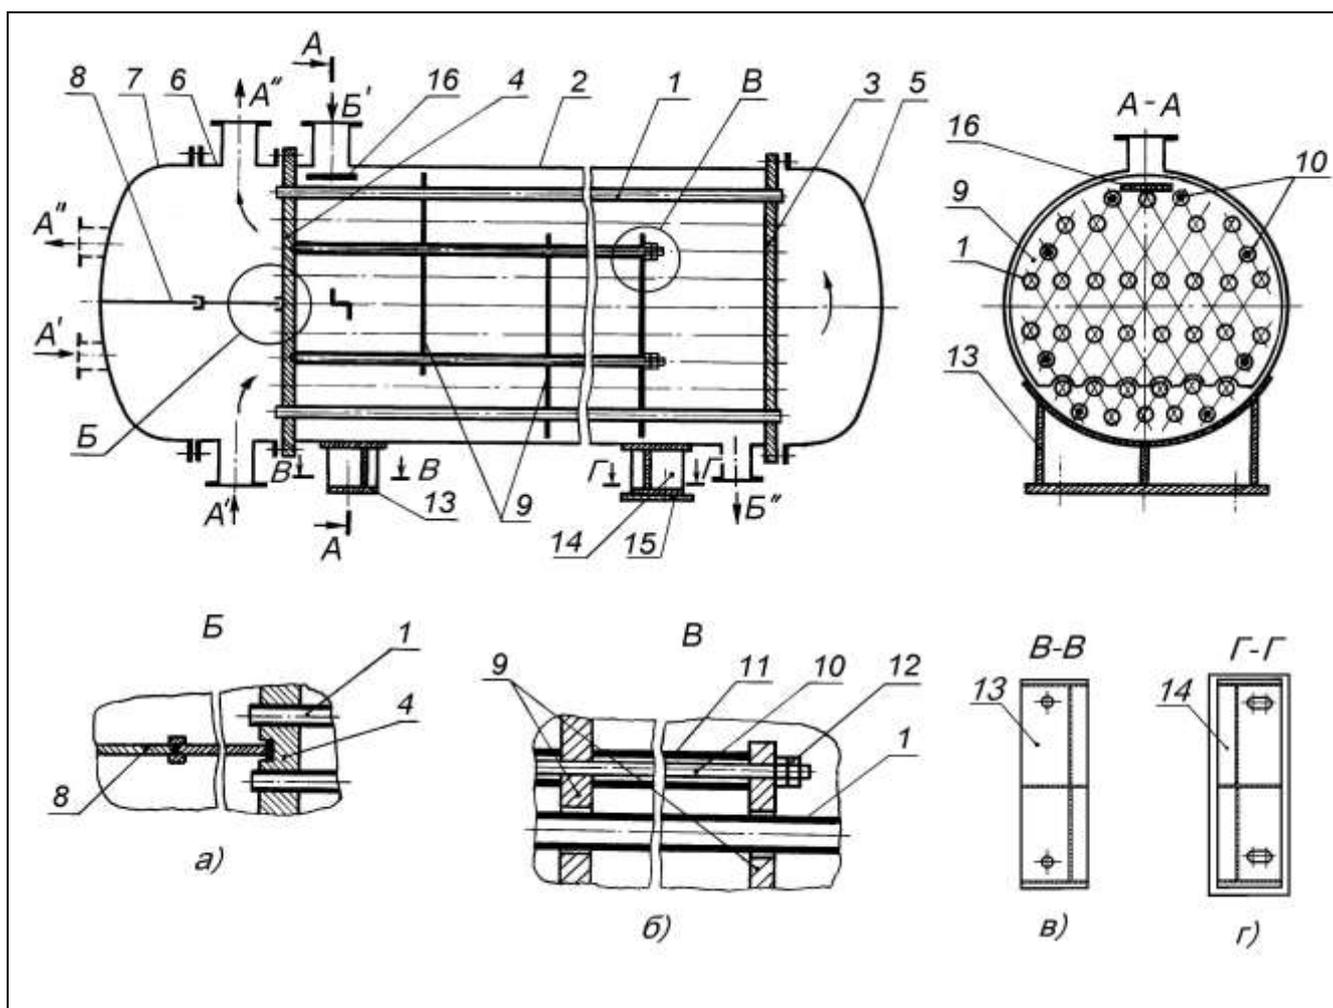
Теплообменник жесткой конструкции с неподвижными трубными решетками типа Н: а) – узел соединения продольной перегородки 8 с трубной решеткой 4; б) – узел соединения поперечных перегородок 9 с помощью стяжек 10; в) – схема размещения отверстий на неподвижной опоре 13; г) – схема размещения отверстий на подвижной опоре 14 с подкладным листом 15
